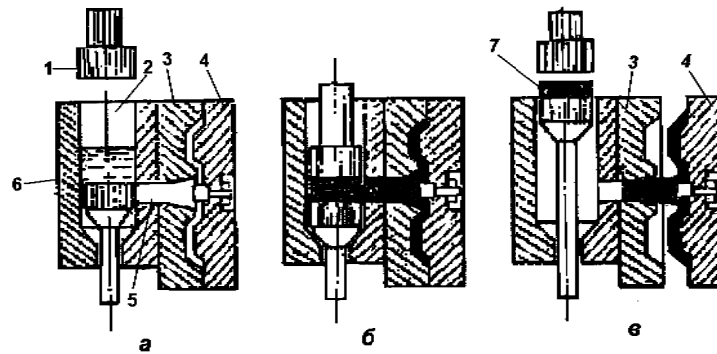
Послідовність процесу лиття під тиском з холодною вертикальною камерою пресування: а-заливання розплавленого металу; б-робочий хід пресуючого поршня; в-видалення виливки.
